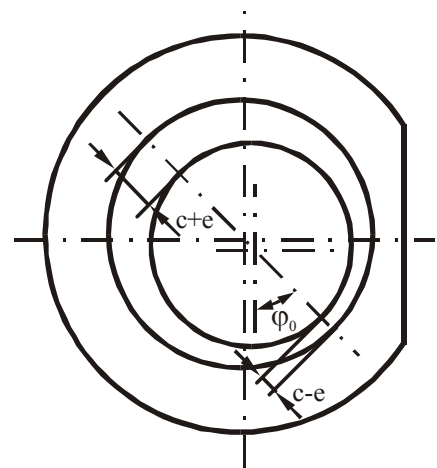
Радиальный зазор в гладком цилиндрическом газовом подшипнике
